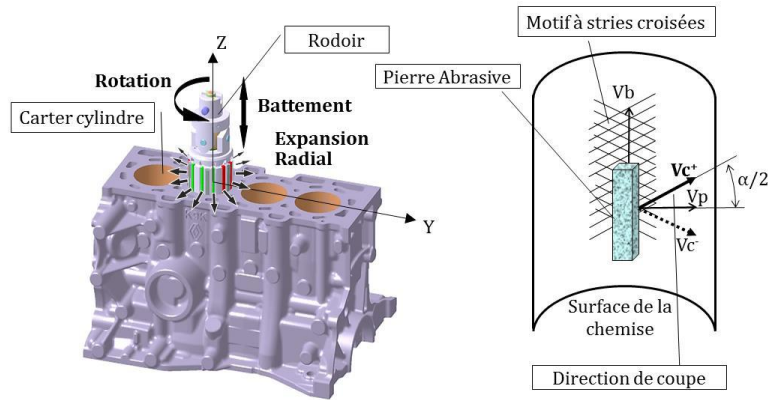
Schéma cinématique d'une machine de rodage [3].
